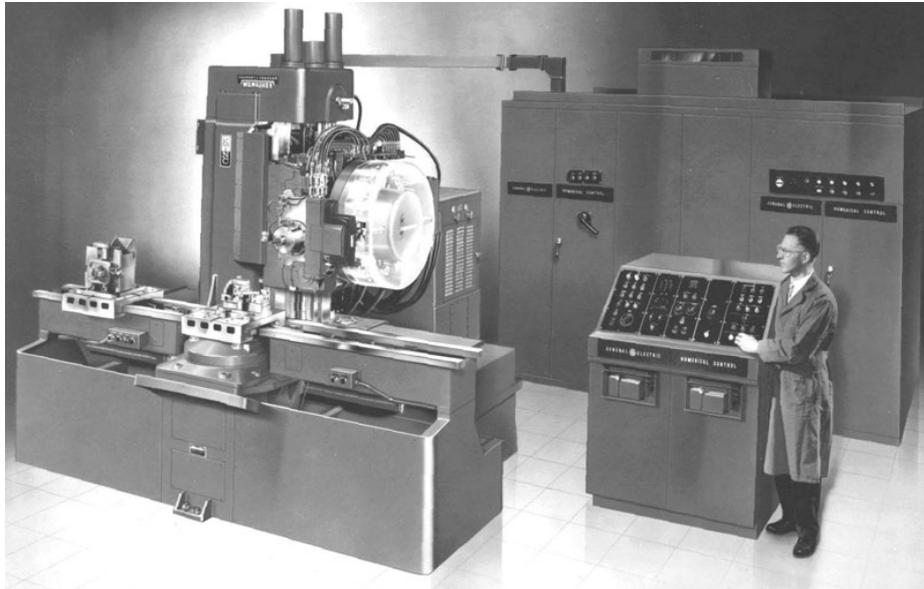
En 1959 se introdujo al mercado la Milwaukke-Matic-II que fue la primer máquina con un intercambiador de herramientas
